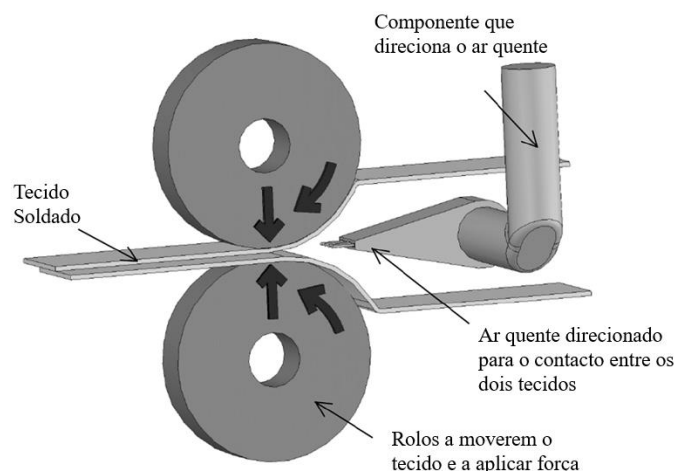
Equipamento de soldadura por Gás quente, adaptado de, *I. Jones & G.K. Stylios (2013)
